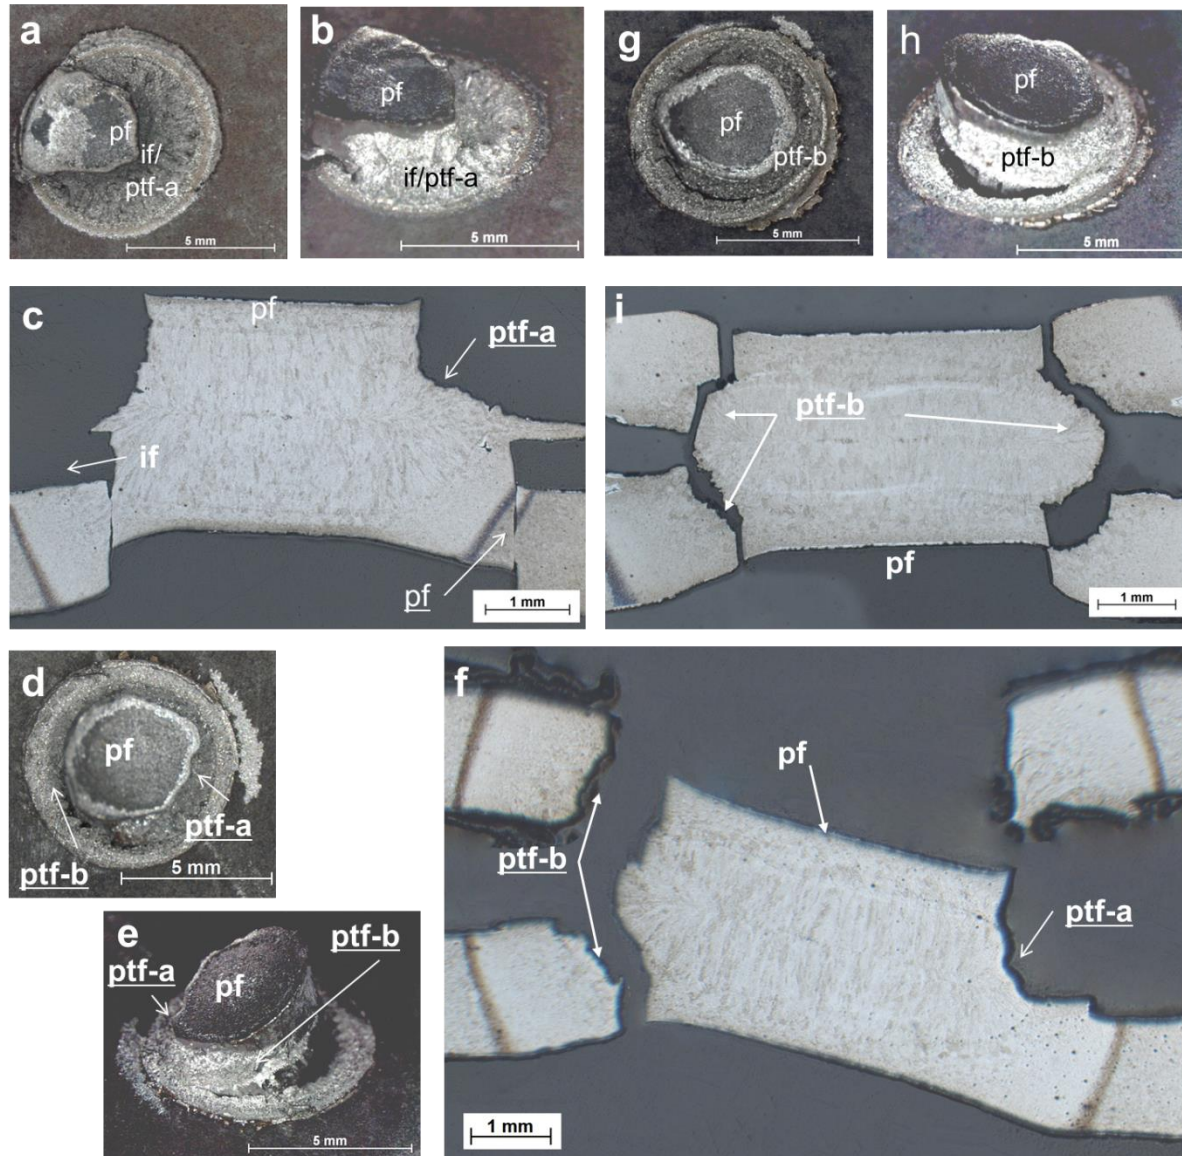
Bruchmodi der Widerstandspunktschweißverbindungen: Abgleich zwischen Sichtprüfung und Schliffbild aus [43]
